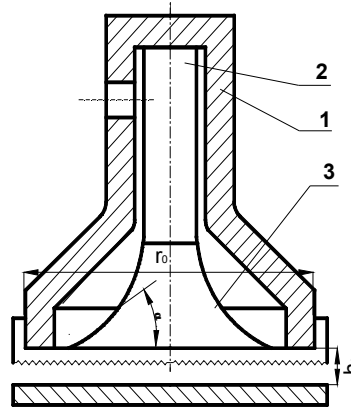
Конструктивна схема струменевого ежекційного захоплювача за плоску поверхню
